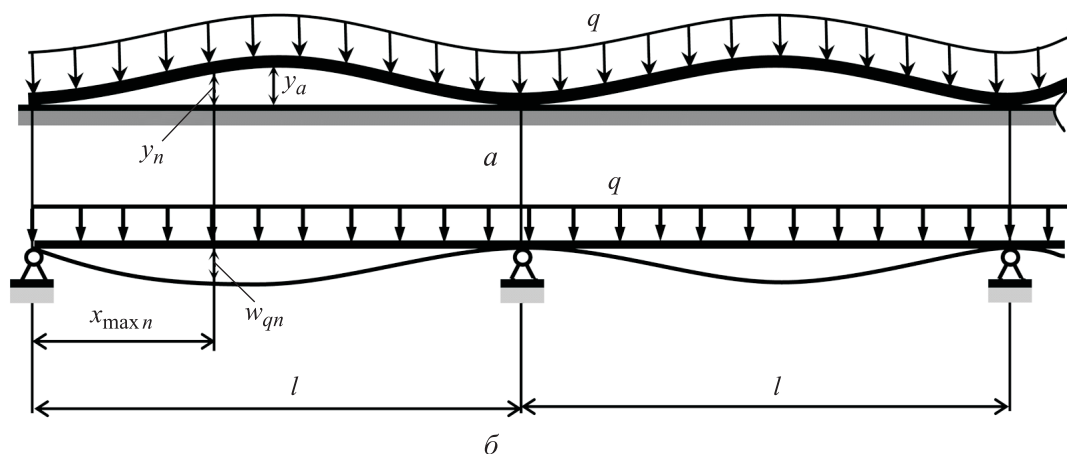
Расчетная схема призматической заготовки при закреплении магнитным полем стола станка: а — схема заготовки с приложенной нагрузкой; б — расчетная схема неразрезной балки
